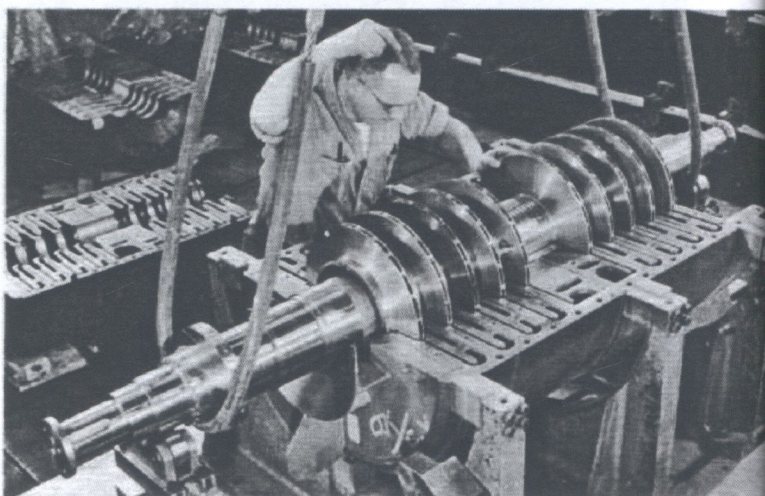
Монтаж ротора у внутрішньому корпусі
